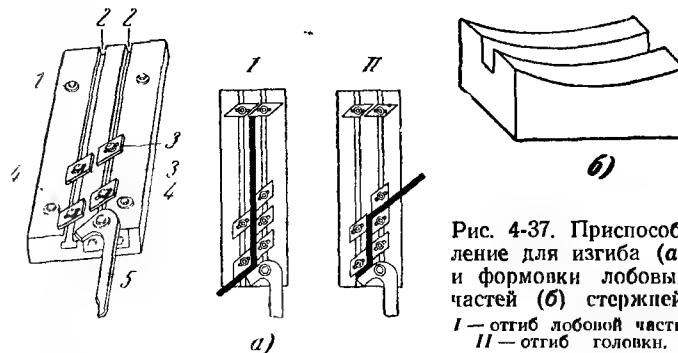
Приспособление для изгиба (а) и формовки лобовых частей (б) стержней.
